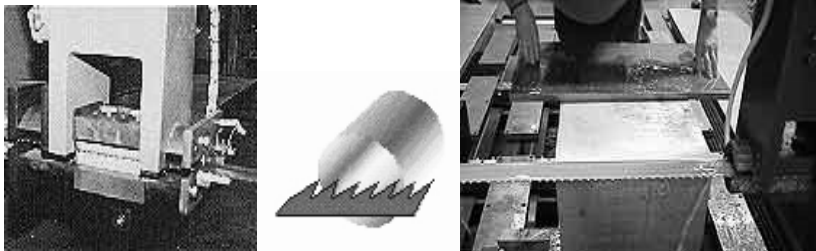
Разрезка заготовок в горизонтальном направлении
